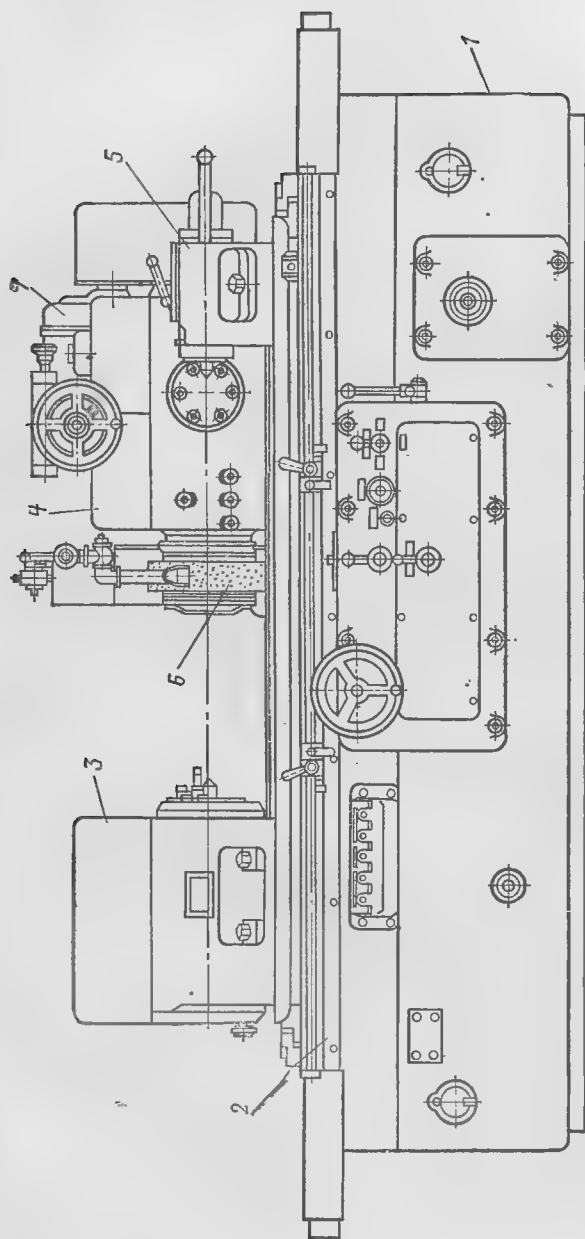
Общий вид круглошлифовального станка модели 3151.
